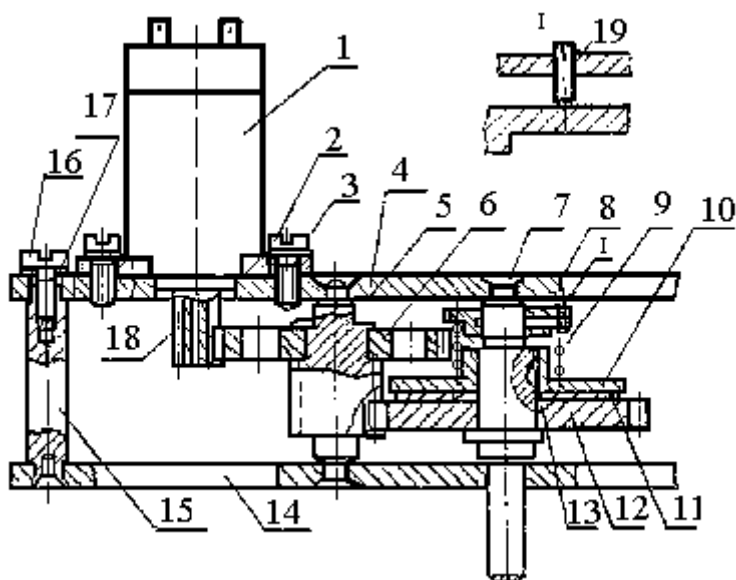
Фрагмент чертежа общего вида приборного редуктора с перечнем элементов
